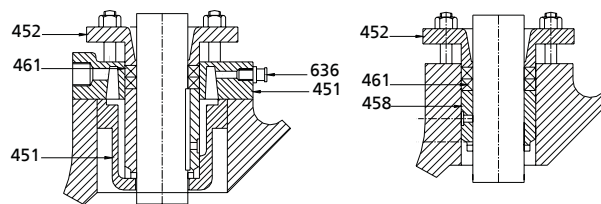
Stopfbuchsgehäuse für Wellenschutzrohr
